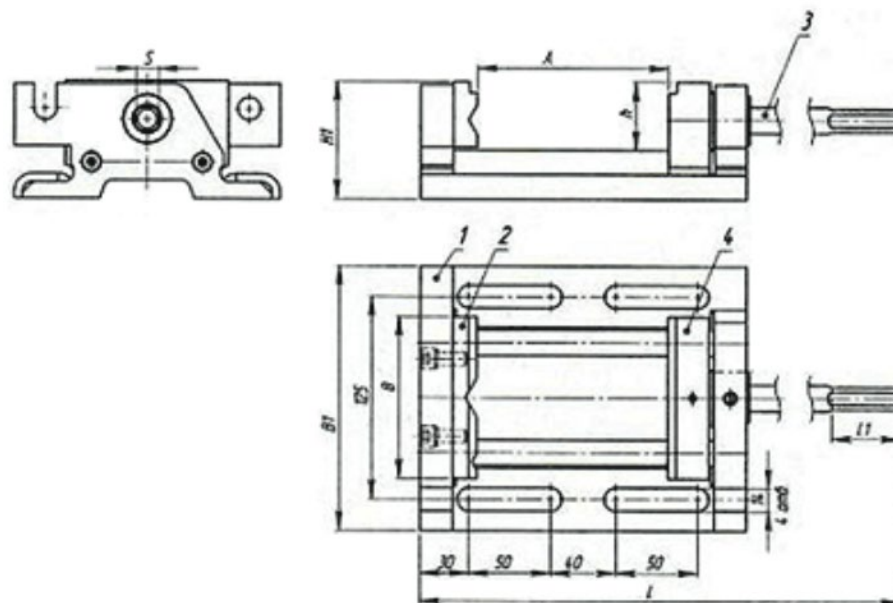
Схема верстатних лещат: 1-корпус, 2- змінна затискна планка нерухомої губки, 3 – гвинт, 4 – губка рухома
